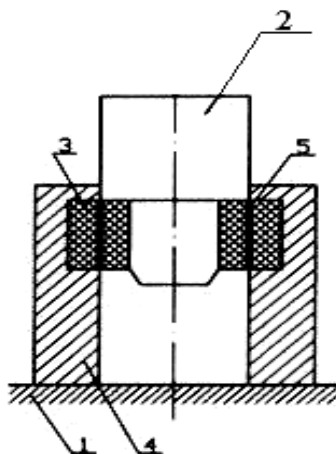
Схема испытания раструбного соединения на сдвиг:
